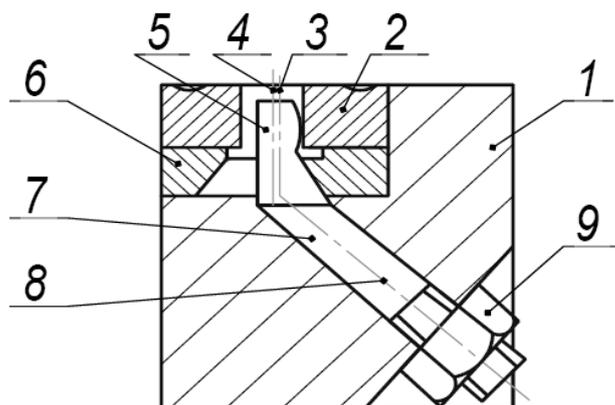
Сборный резец по авторскому свидетельству № 994133 (конструкция 6)
